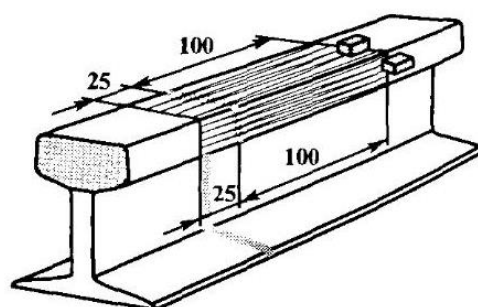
Схема прозвучивания головки сверху и с боковых поверхностей в сварного стыка.
